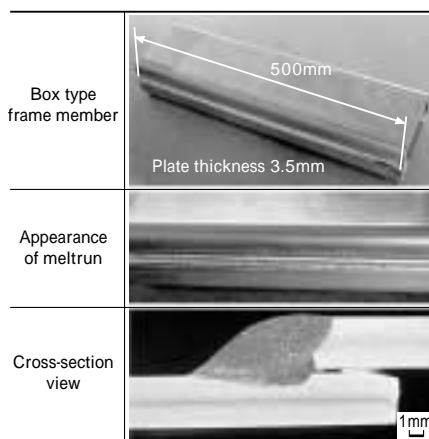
後付型サーボ式ブルトーチにて得られた実用的溶接の品質例（母材：A5454P-H112，溶接電流：200A，溶接速度：120cm/min）
